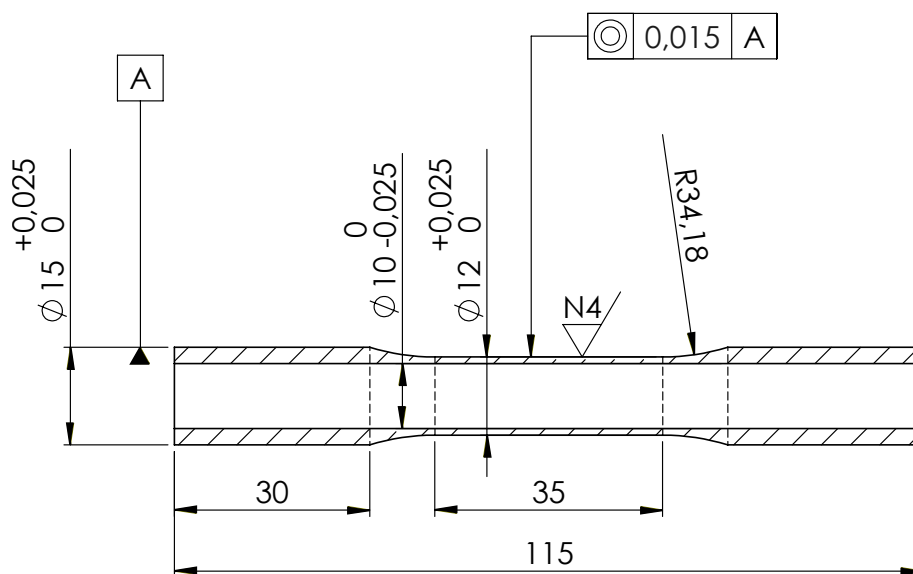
Geometria dos corpos de prova tubulares utilizados nos ensaios torcionais, denominados 304L-TUB. Dimensões em milímetros.
